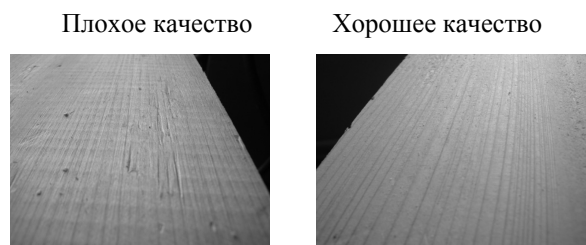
Качество обработанных поверхностей методом цилиндрического фрезерования
